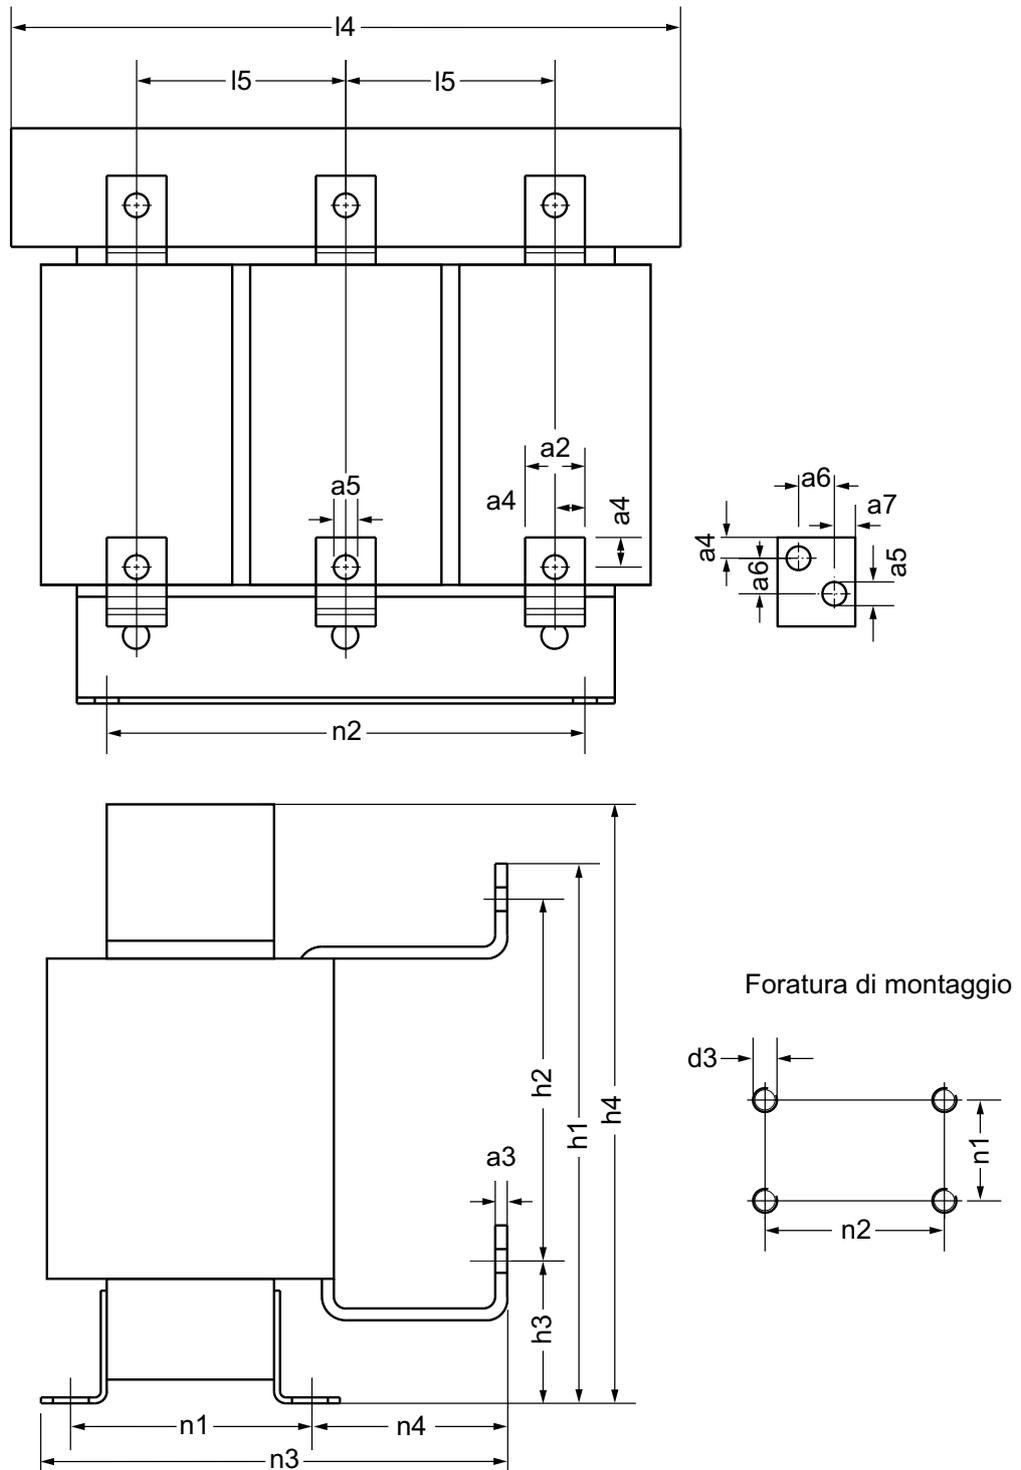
Disegno quotato bobina di rete per Basic Line Module
